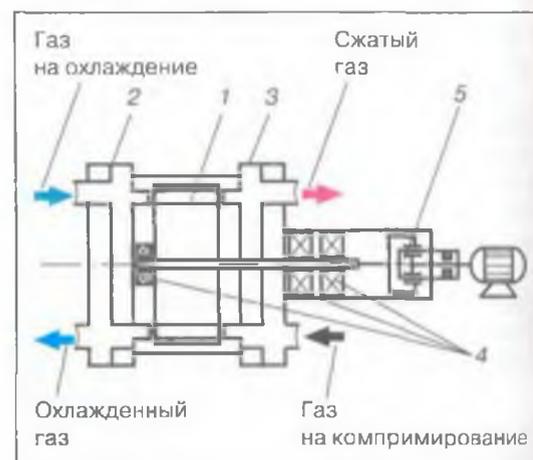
Турбодетандер: 1 — ротор; 2 — осевая турбина; 3 — центробежный компрессор; 4 — радиальные подшипники; 5 — осевой упорный подшипник.
